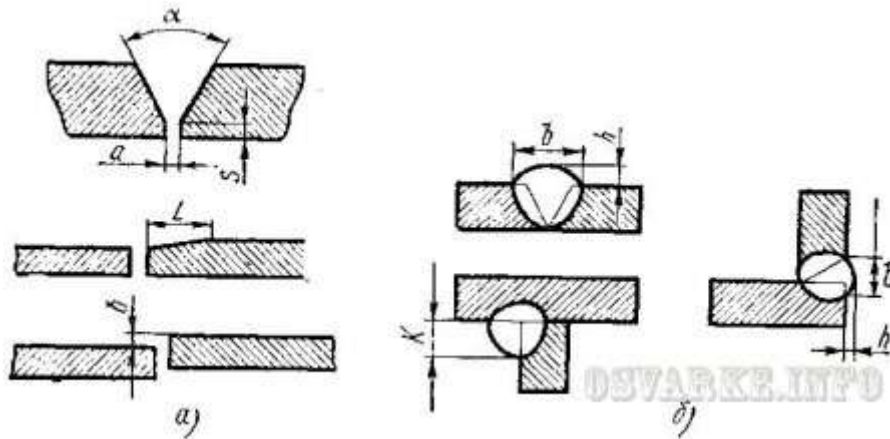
Элементы геометрической формы подготовки кромок под сварку и шва .
